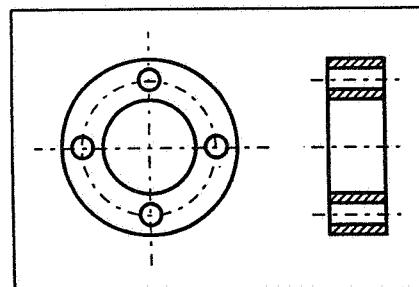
Le indicazioni relative alla sezione (ingrossamento degli estremi della traccia, frecce direzionali e lettere alfabetiche) non sono obbligatorie quando la posizione del piano di sezione è inequivocabile.
